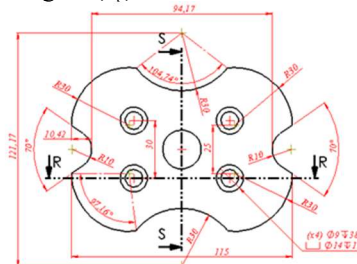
Desenho esquemático do corpo de prova (dimensões em mm).
